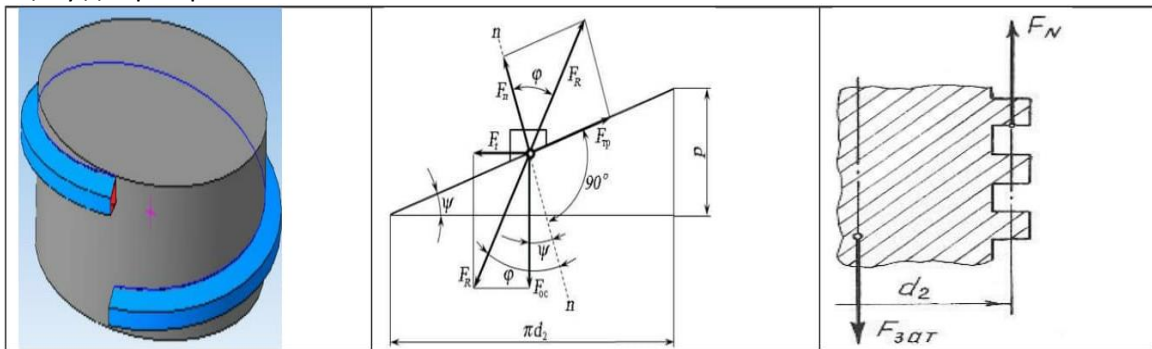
Вихідні зображення для вивчення явища самогальмування у передачі гвинт-гайка з прямокутною різьбою: виток різьби; розгортка витка різьби з нанесеними силами (розрахункова модель передачі гвинт-гайка); схема зрівноваження осьової сили нормальною реакцією робочої грані різьби
